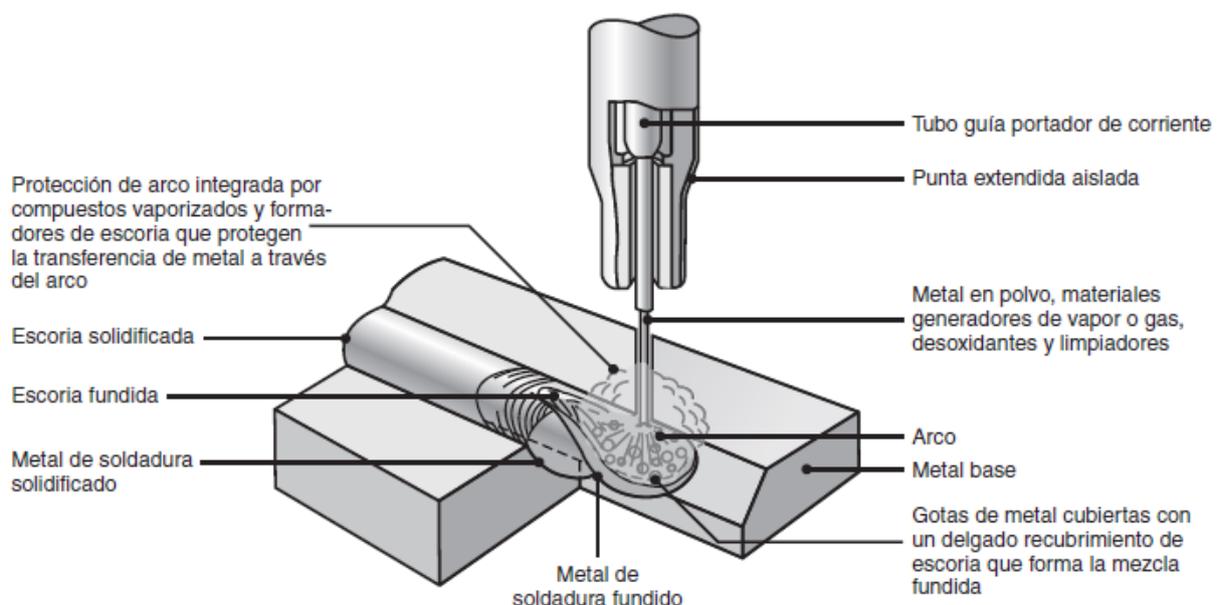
Soldadura por arco con núcleo de fundente (Fuente: *Manufactura, Ingeniería y Tecnología*)
